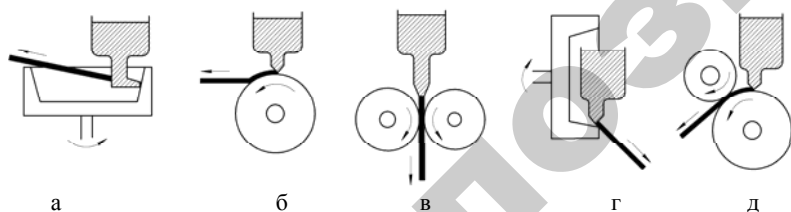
Методы получения тонкой ленты путем закалки из расплава: а — центробежная закалка; б — закалка на диске; в — прокатка расплава; г — центробежная закалка; д — планетарная закалка
